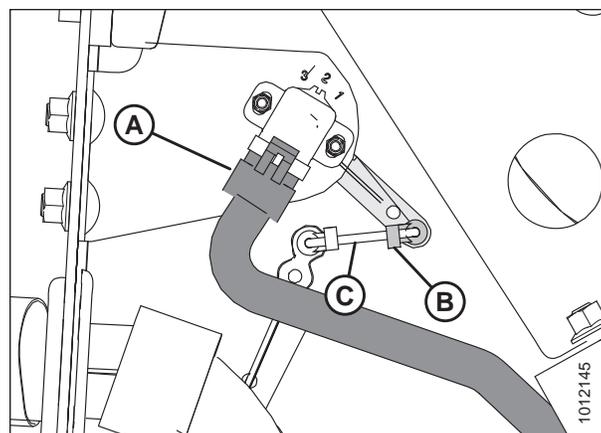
Ensamblaje del sensor de altura de la plataforma; lado izquierdo
